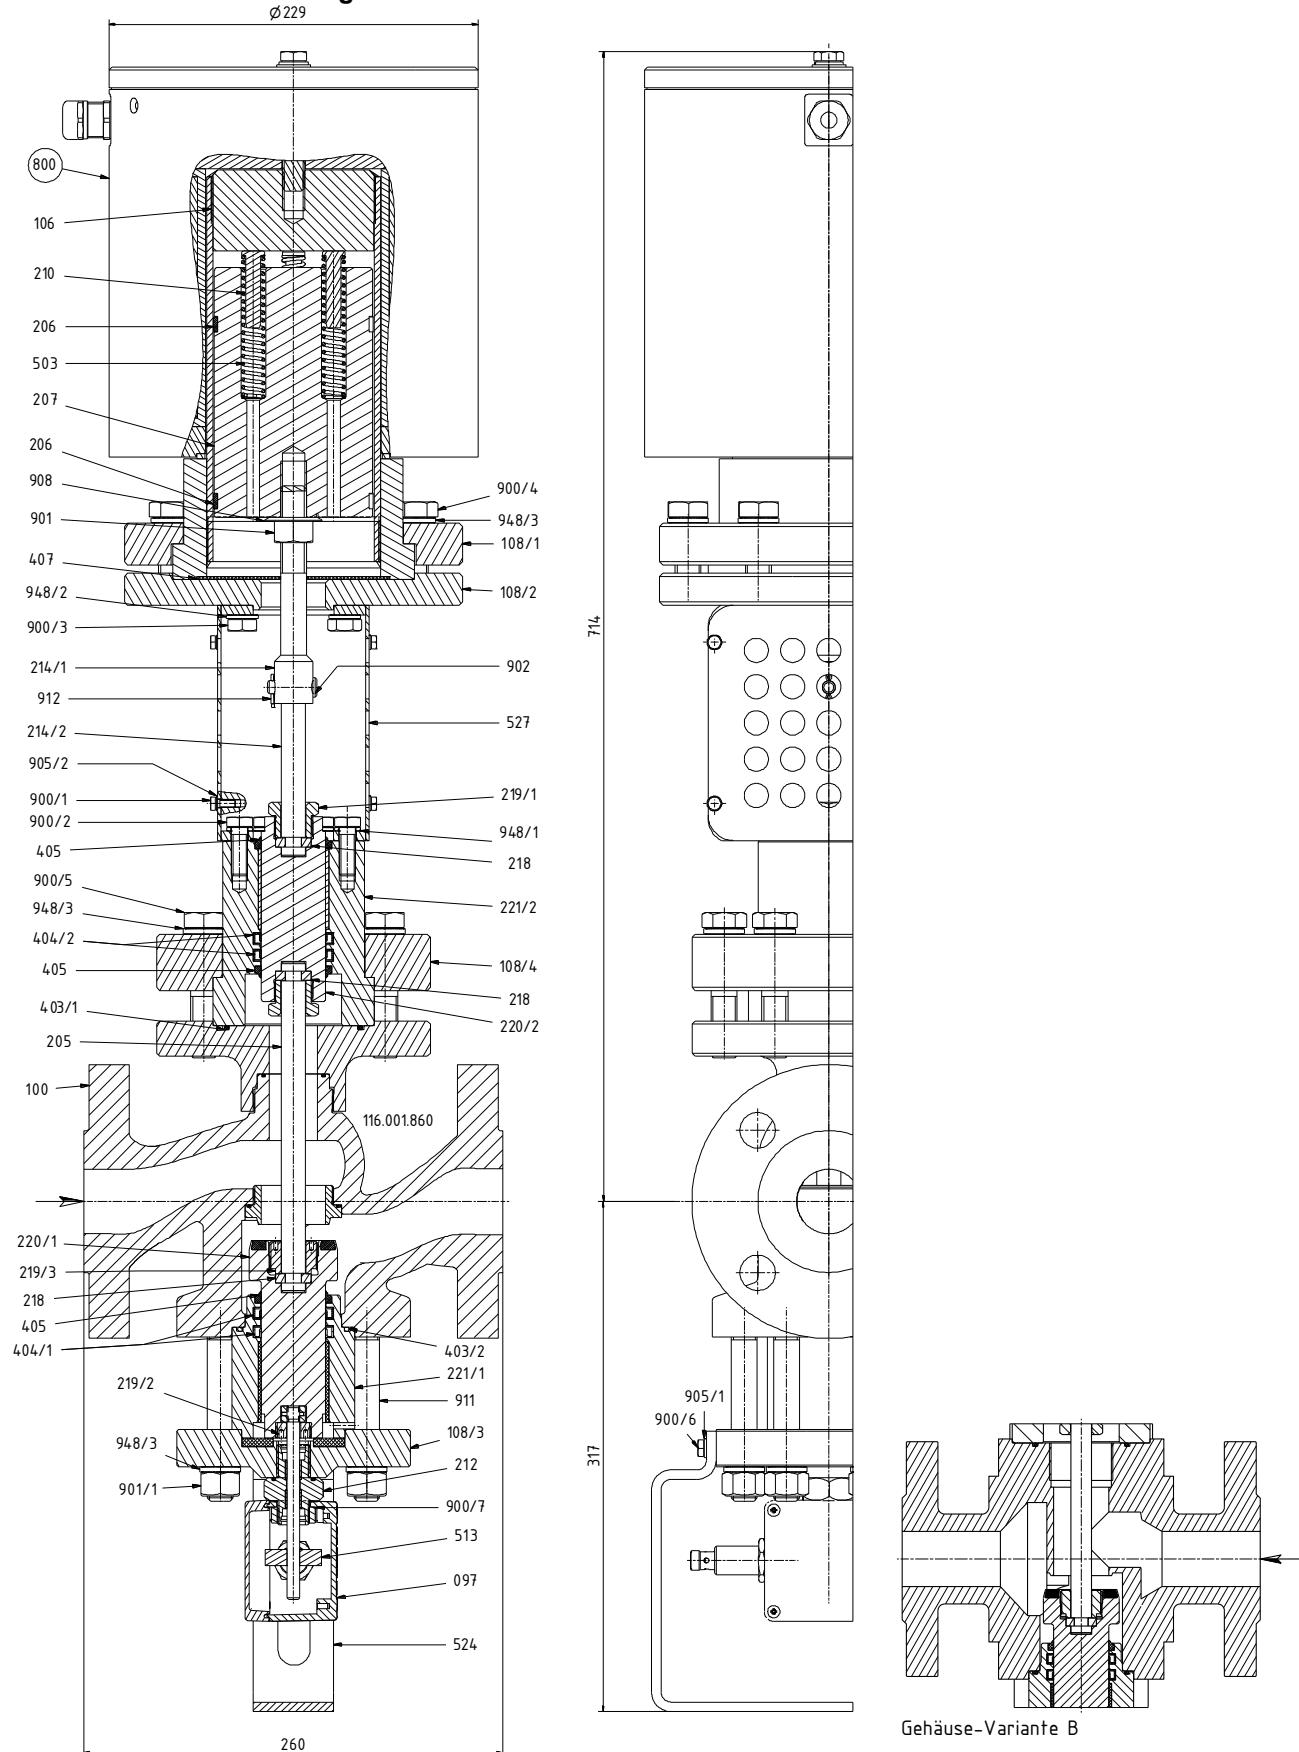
Flanschausführung 40-EVSO 5NH...
